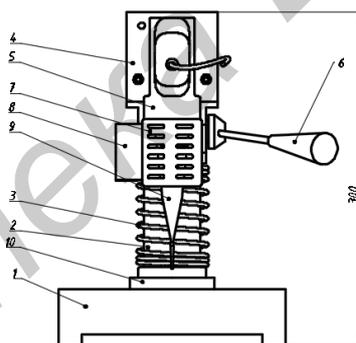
Конструкция технологического устройства УЗ сварки
